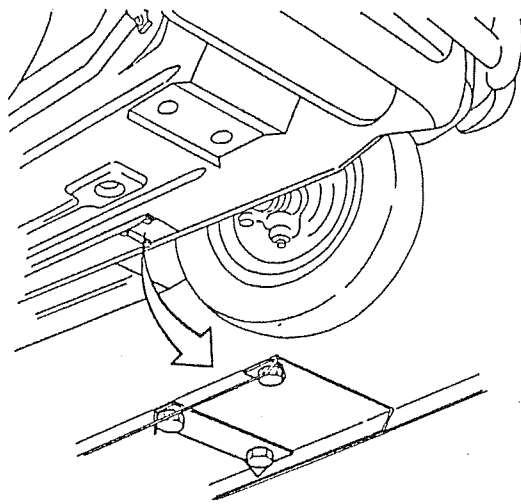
Skruvar och låsbleck, främre lagerkonsol.
